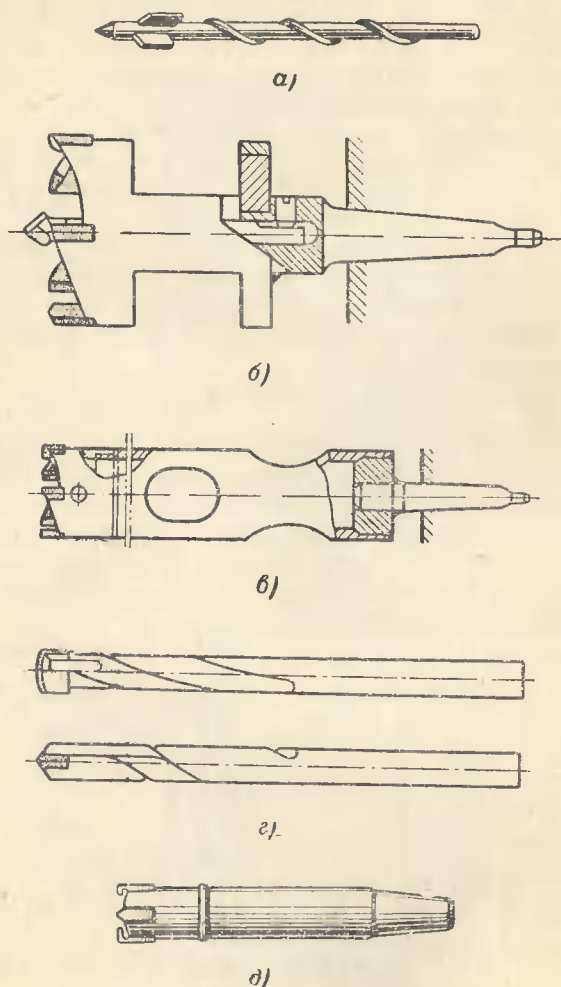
Инструменты с пластинками из твердых сплавов для дыропробивных работ.
